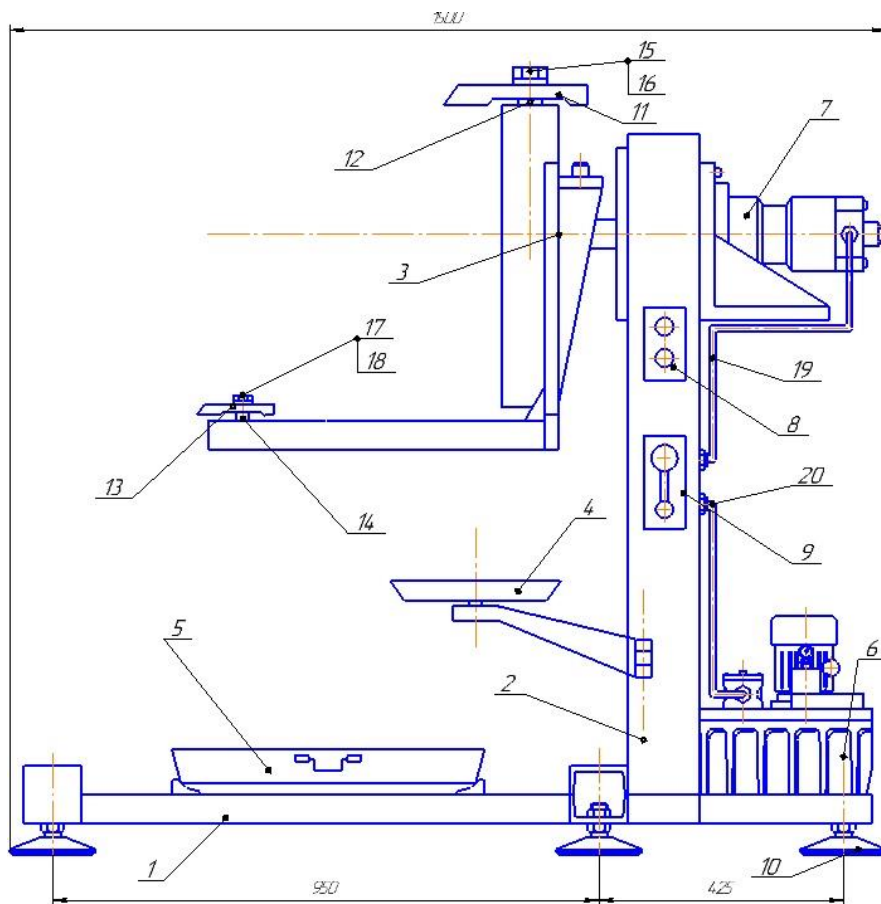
Загальний вид конструкції станда-кантувача: 1 – основа; 2 – стійка приводна; 3 – супутник; 4 – корзина; 5 – корито; 6 – насосна станція; 7 – гідромотор; 8 – пульт керування; 9 – розподільник; 10 – опора; 11 – прихват; 12, 14 – шпилька; 13 – прижим; 15, 17 – гайка; 16, 18 – шайба; 19 – рукава; 20 – роз’ємні з’єднання рукавів
